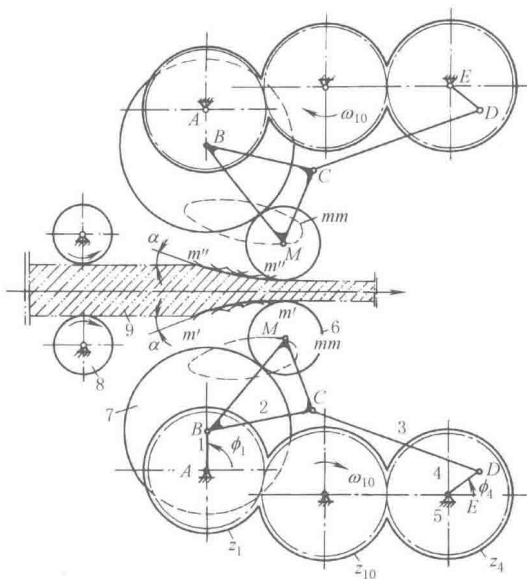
轧钢机中的五杆-齿轮组合机构
